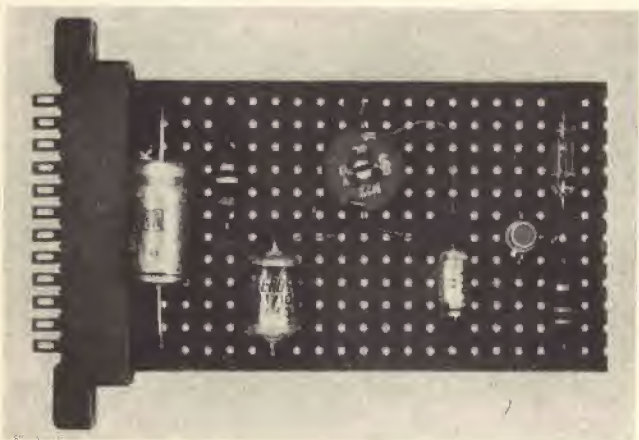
Prototipo dell'oscillatore bloccato di figura 1 a montaggio ultimato.
